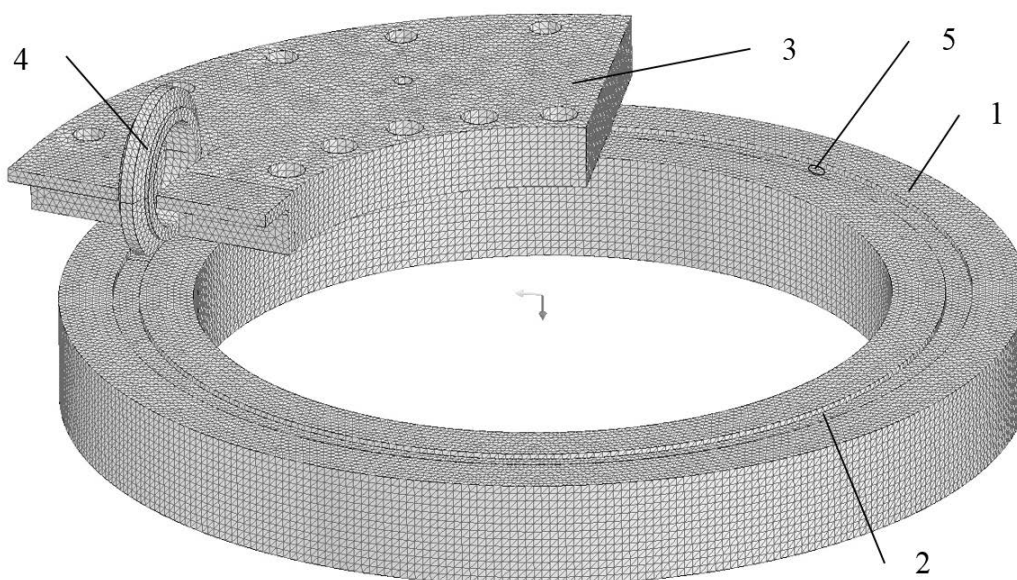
Конечно-элементная модель установки СЛИК: 1 – кристаллизатор; 2 – заготовка; 3 – башмак; 4 – прижимной ролик; 5 – место заливки жидкого металла из дозаторного устройства
